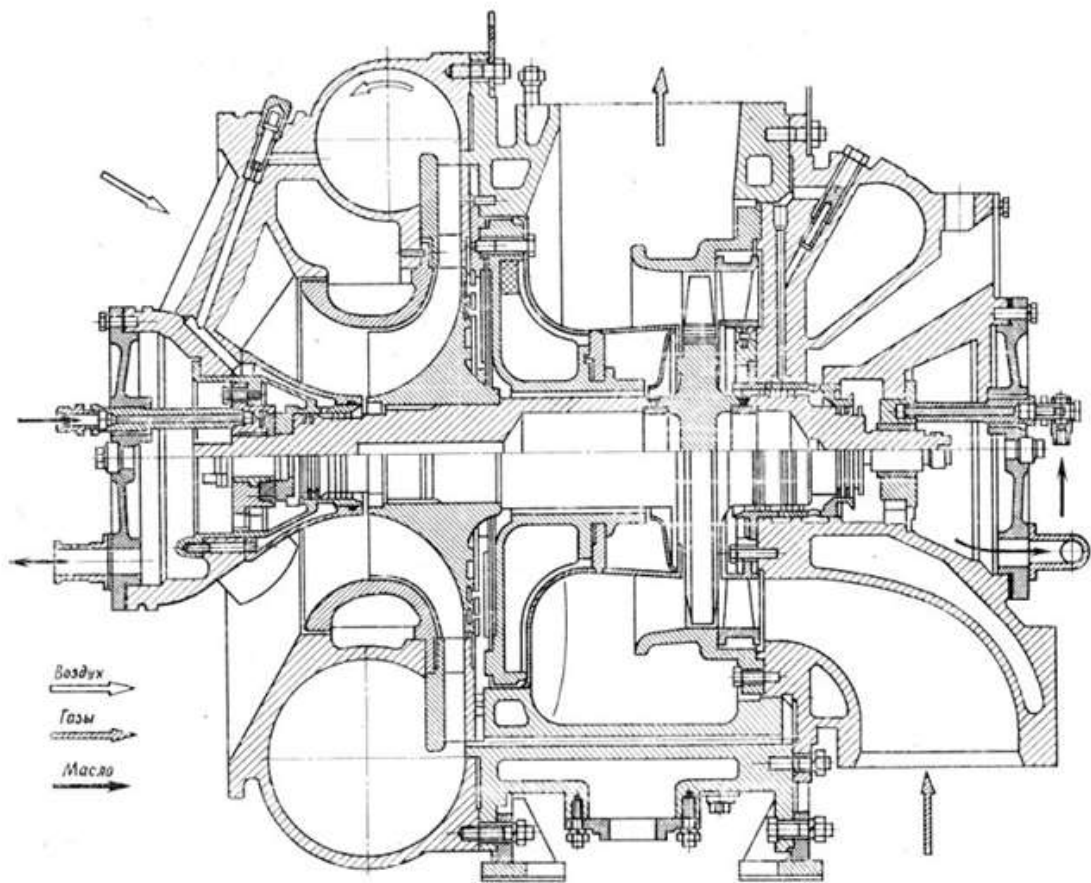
Поперечний розріз турбокомпресора ТК-23
